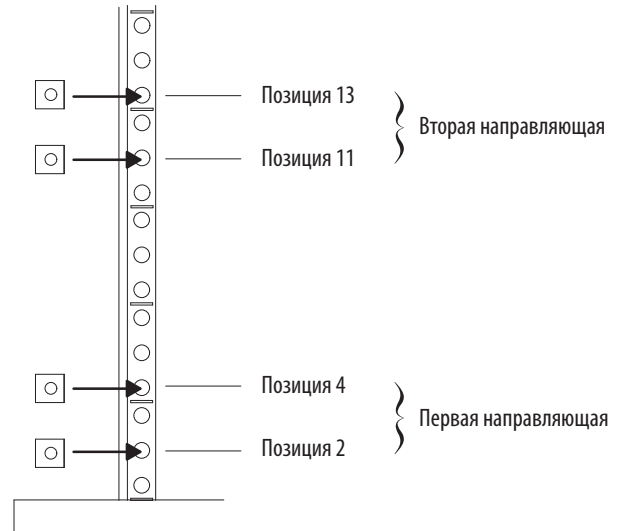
Положения винтов задней направляющей для ЕВМ
